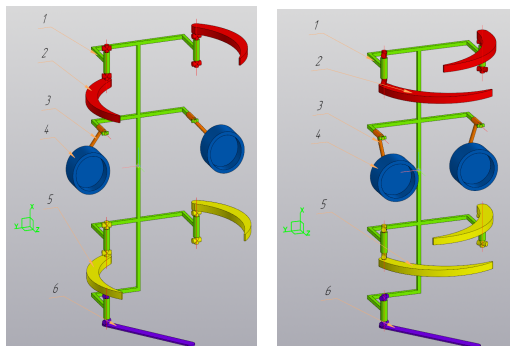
Упрощенная схема линейного механизма захватного устройства: 1 – рама, 2 – верхний сучкорезный нож, 3 – рычаг протяжного вальца, 4 – протяжной валец, 5 – нижний сучкорезный нож, 6 – пильный блок
